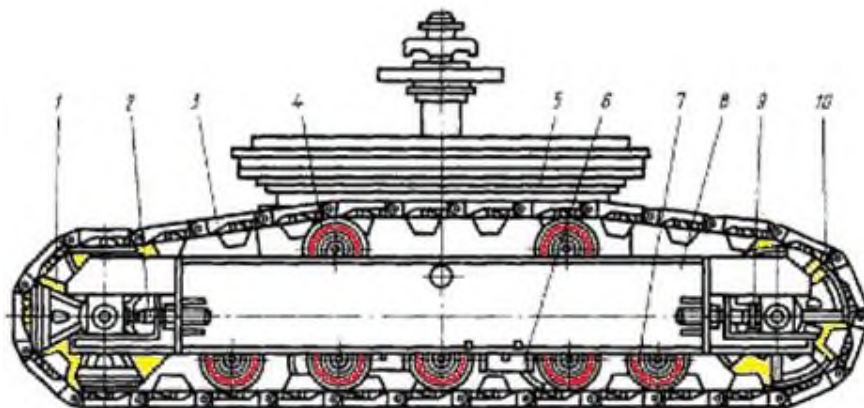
Гусеничная тележка одноковшового строительного экскаватора: 1 - ведущая звездочка; 2 - винт; 3 - звено гусеничной ленты; 4, 7 - катки (поддерживающие и опорные); 5 - рама ходовая; 6 - стопорный механизм; 8 - несущая балка гусеницы; 9 - натяжное устройство; 10 - направляющее колесо
